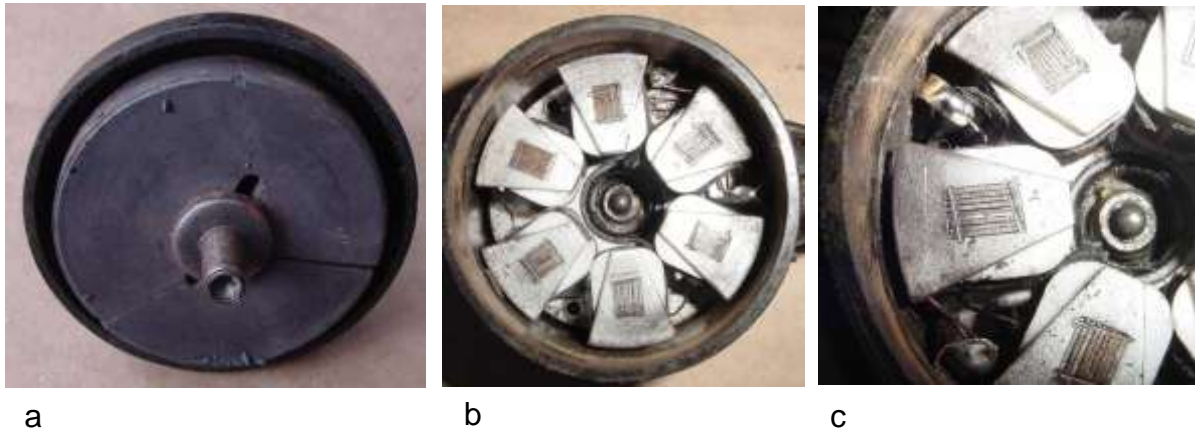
a) Polradscheibe, b) Sechspoliger Anker, c) Stirn- bzw. Polfläche des geblechten Spulenkerns
